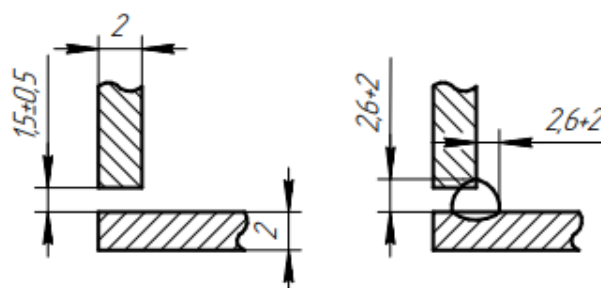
Подготовка кромок и форма шва сварного соединения
